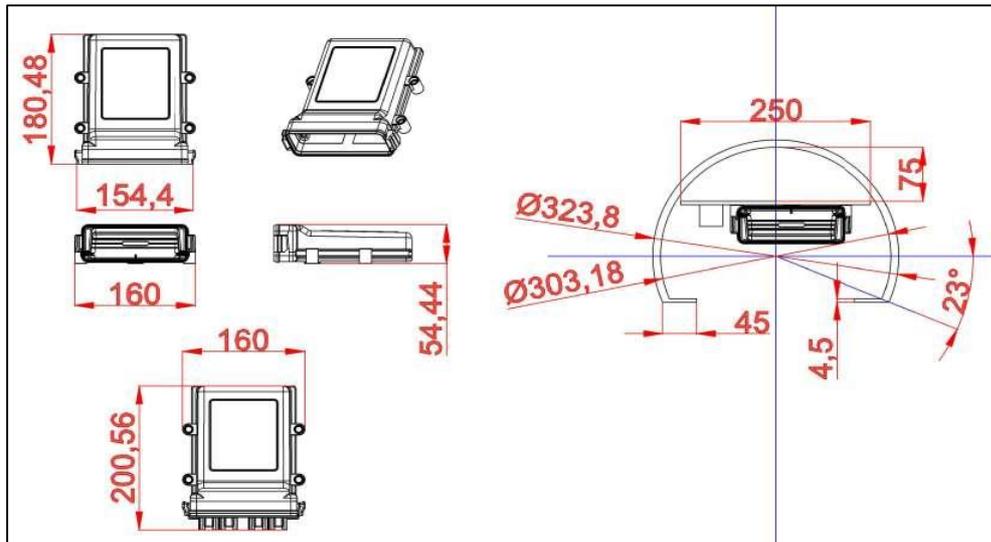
Vista de Planta Controlador DiverBiss, instalación propuesta dentro de poste de monitoreo remoto
